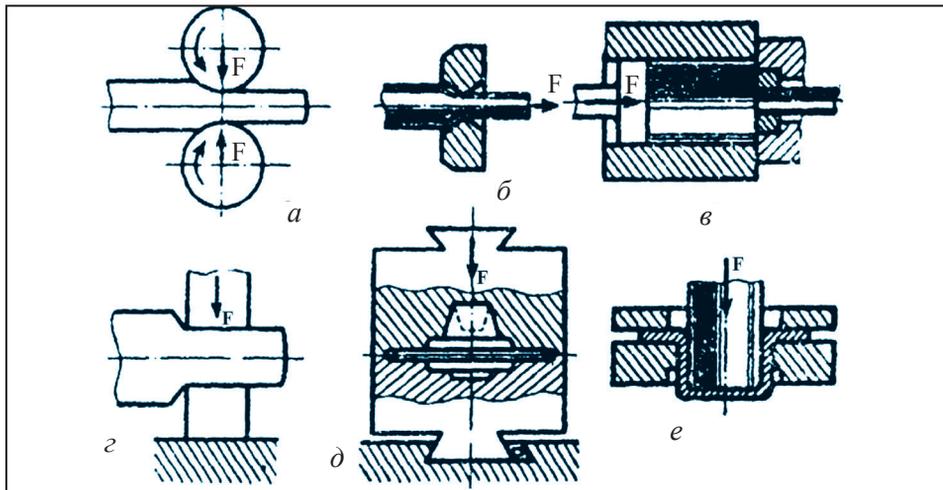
Обработка металлов под давлением: *a* – прокатка; *б* – волочение; *в* – прессование; *г* – ковка; *д* – горячая объёмная штамповка; *е* – холодная листовая штамповка.
